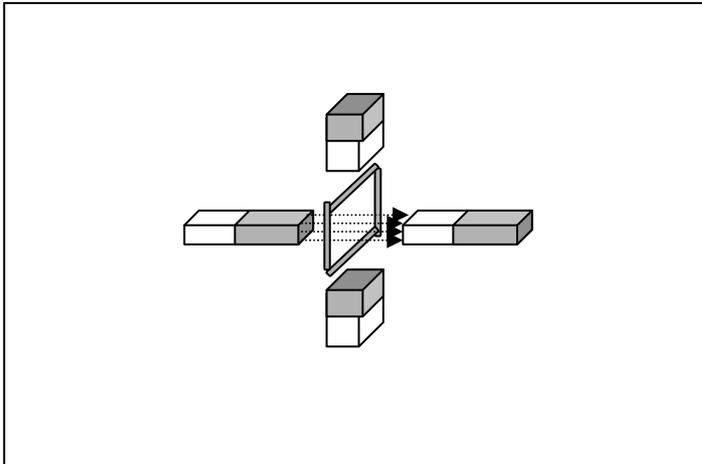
Inserção do bobinado de partida na posição perpendicular.
